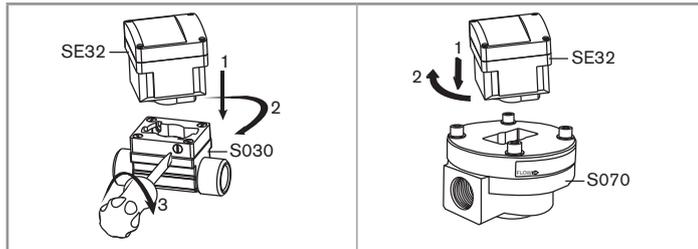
Montieren des SE32 auf das Fitting S030 oder S070
